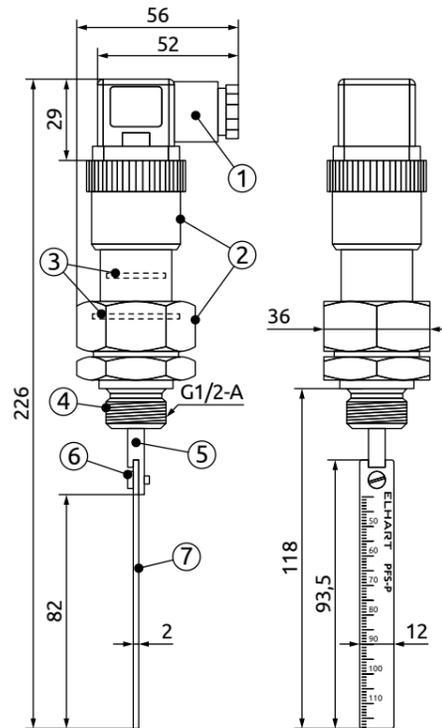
Габаритные размеры реле и сменного лепестка, обозначения элементов конструкции
